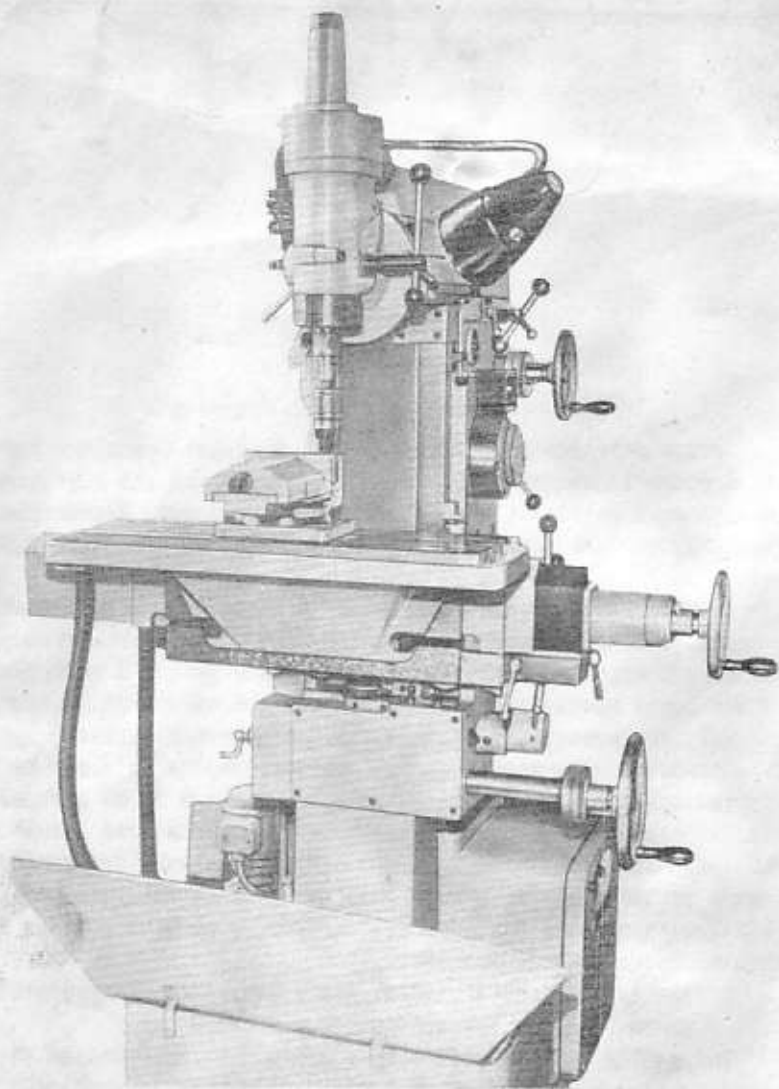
Рис. I. Инструментальный широкоуниверсальный фрезерный станок 675П.
